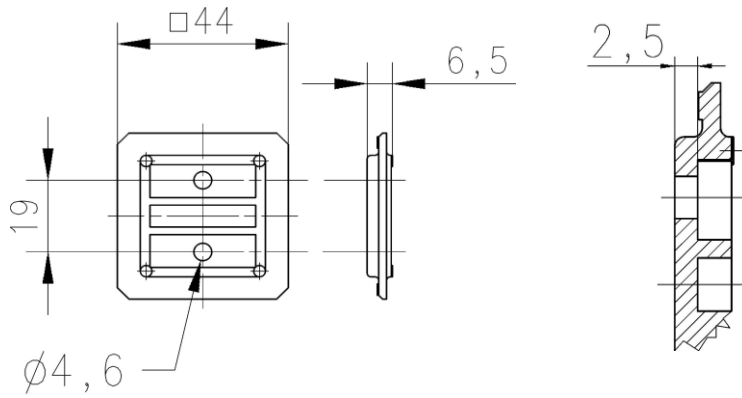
Габаритные и установочные размеры монтажной пластины
